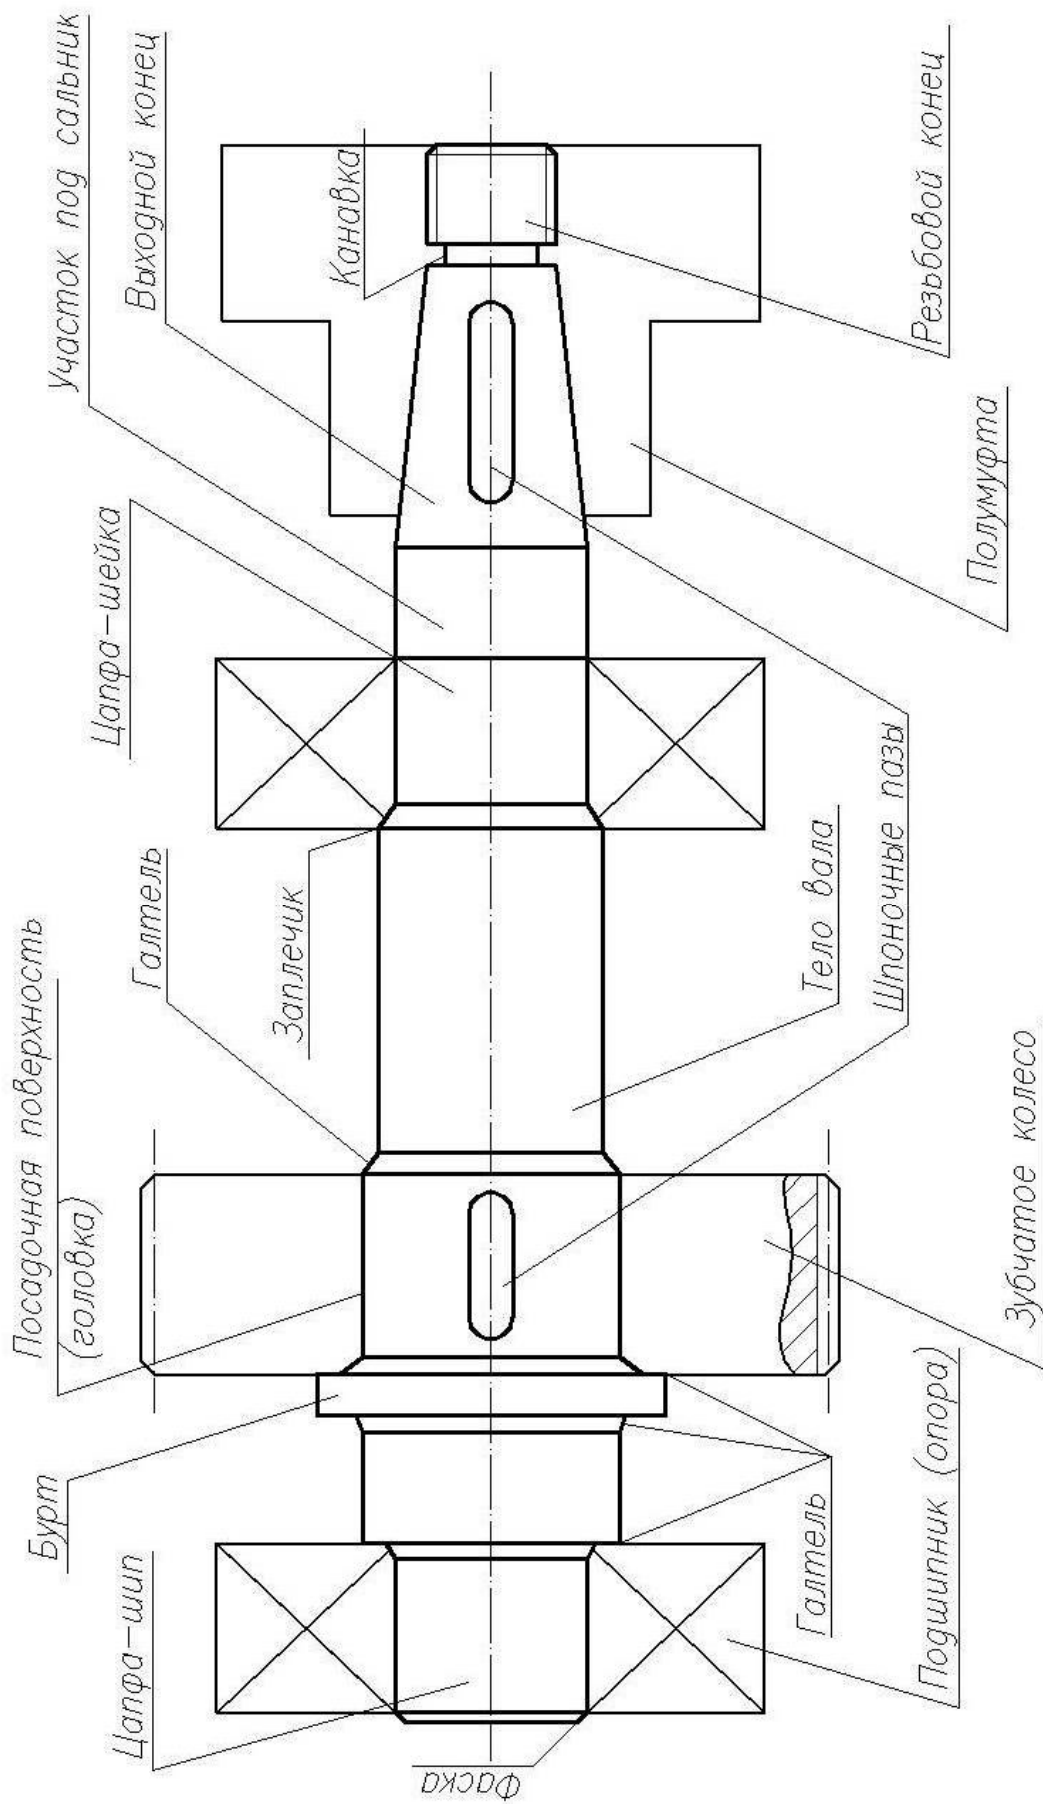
Основные элементы конструкции ступенчатого вала в сборе
